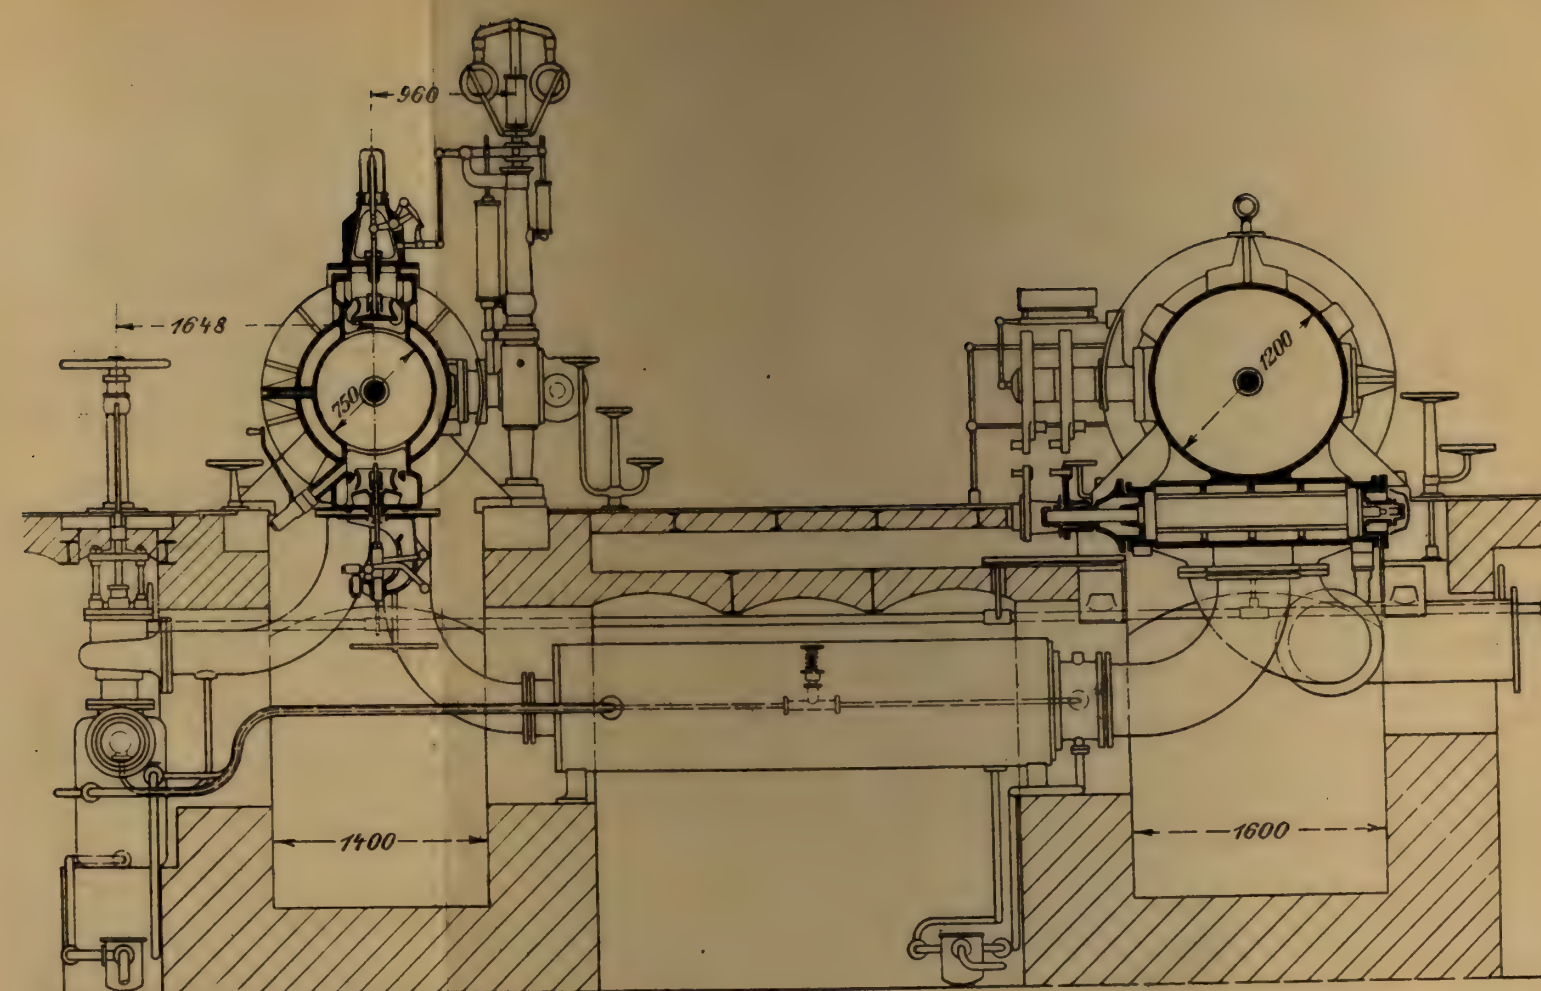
Senkrechter Querschnitt durch die Steuerung des Hoch- und Niederdruckzylinders.
